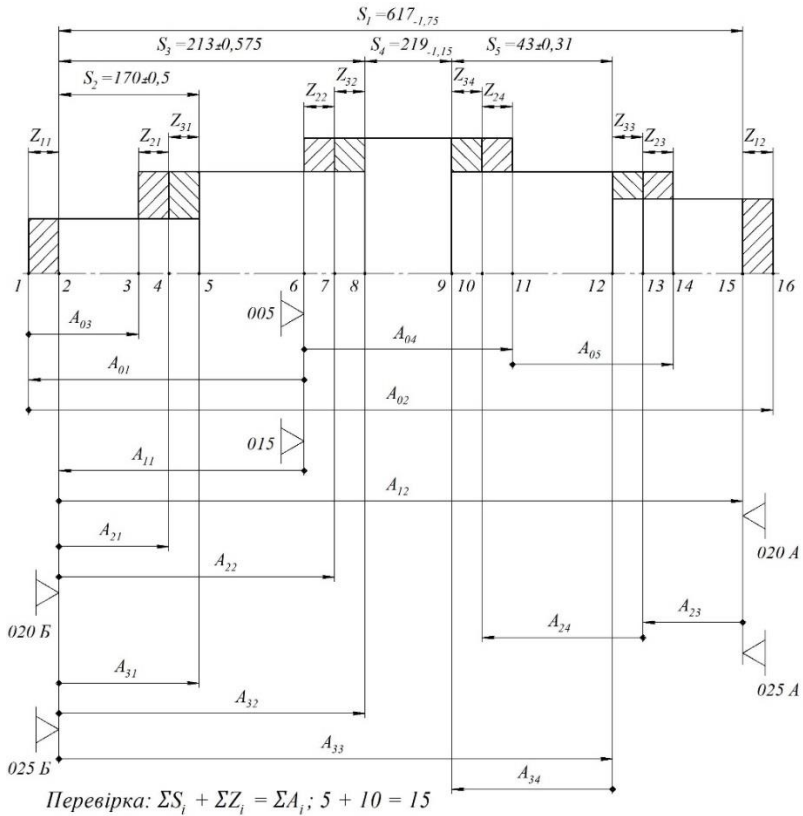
Технологічна схема оброблення торцевих поверхонь заготовки вала FSK-0001.00.327
